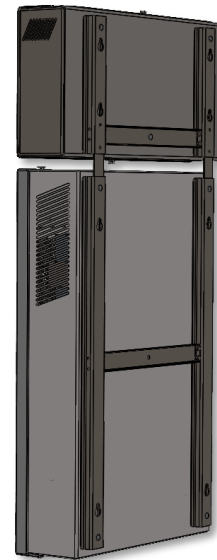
Сборка ЦБ МЕТА 17950/17951, бокса АКБ МЕТА 17901 и кронштейна DR-2109.
